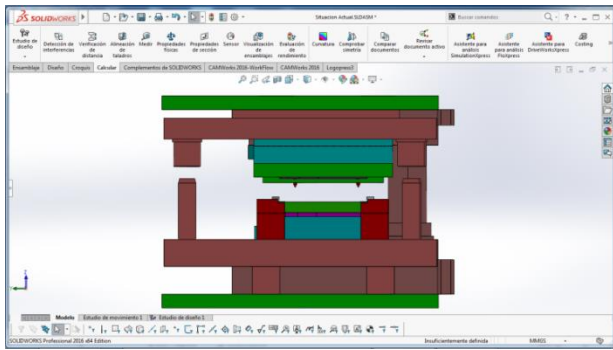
“Troquel Op. 20 Vista Izquierda”
